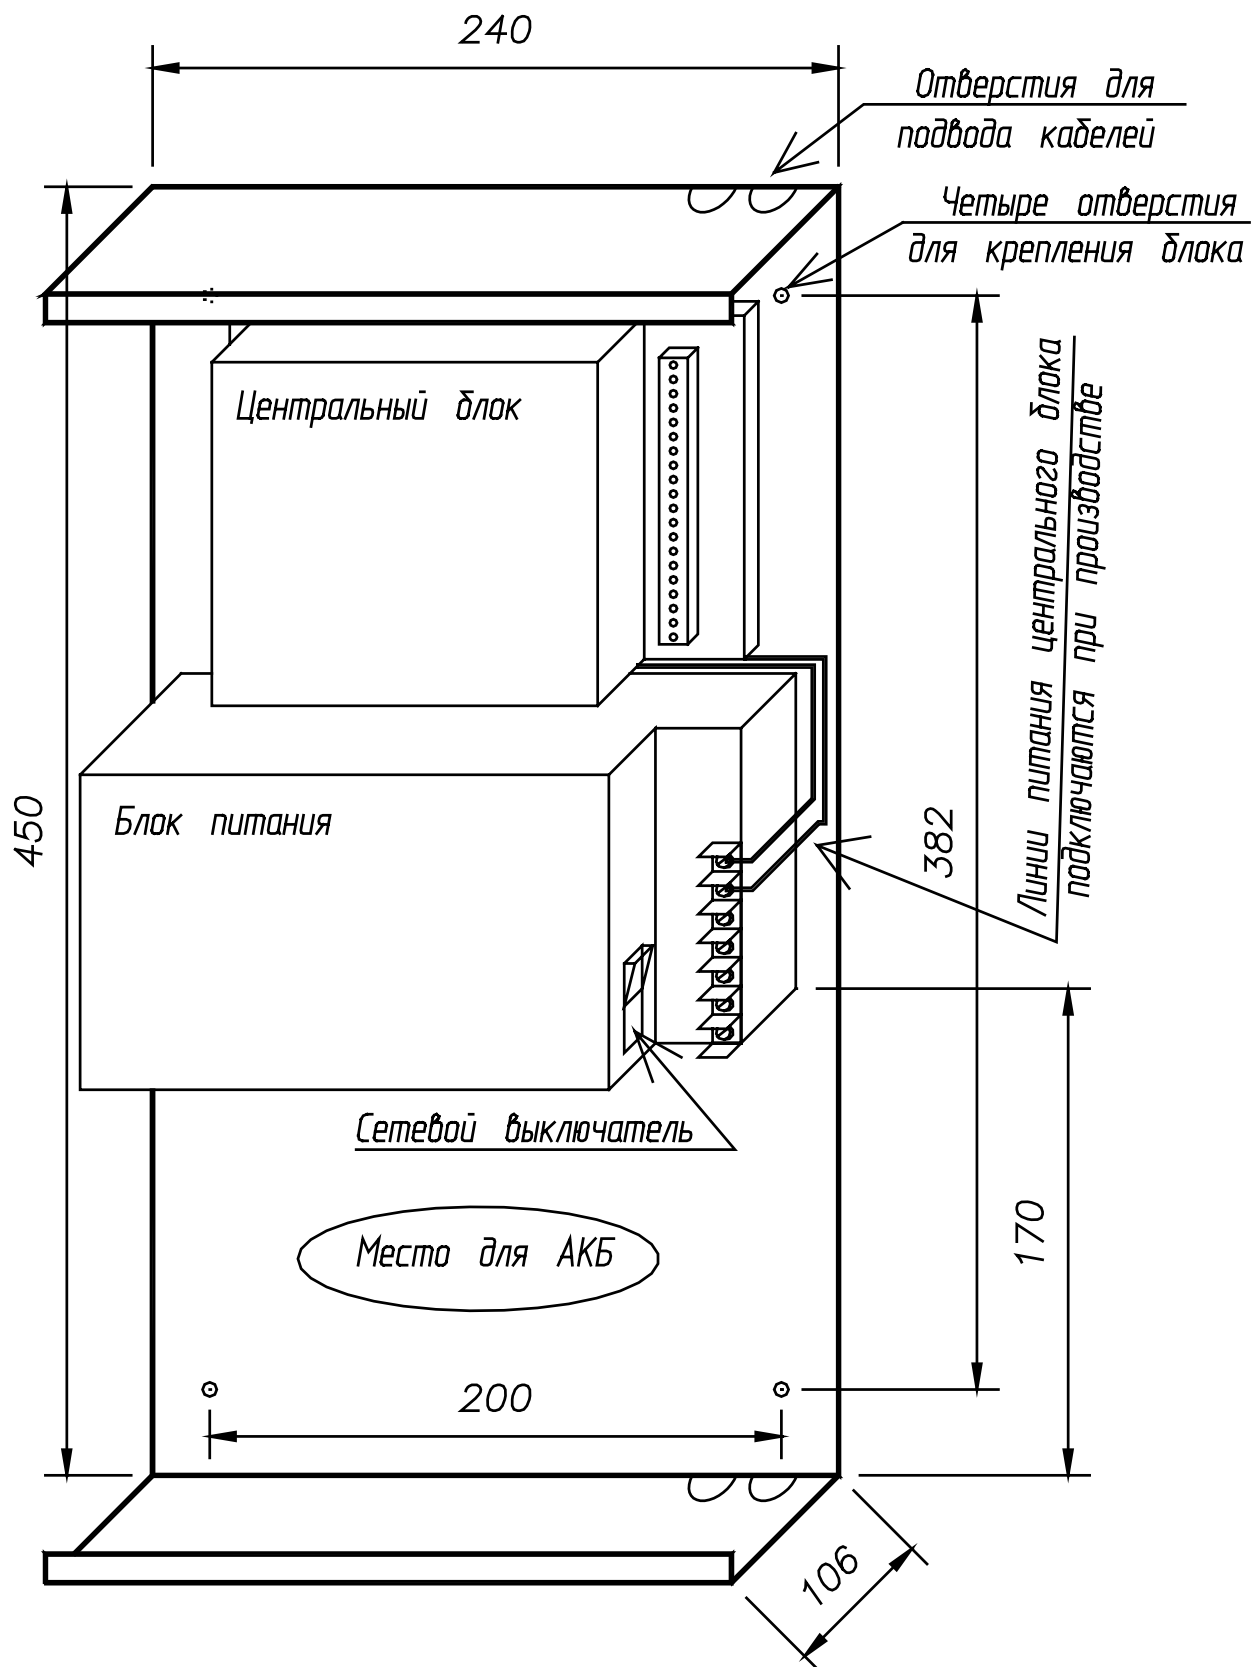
Габаритные и установочные размеры центрального блока ПКП-16, его компоновка
